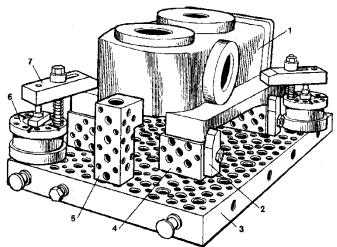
21 Приспособление для установки корпуса редуктора Приспособление на рис. 10.21 предназначено для базирования и закрепления заготовки корпуса редуктора при обработке на многоцелевых станках с ЧПУ.
